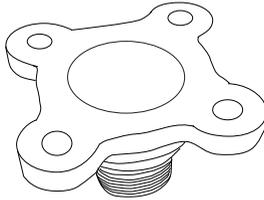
Markieren der Löcher für die Flanscbefestigung
